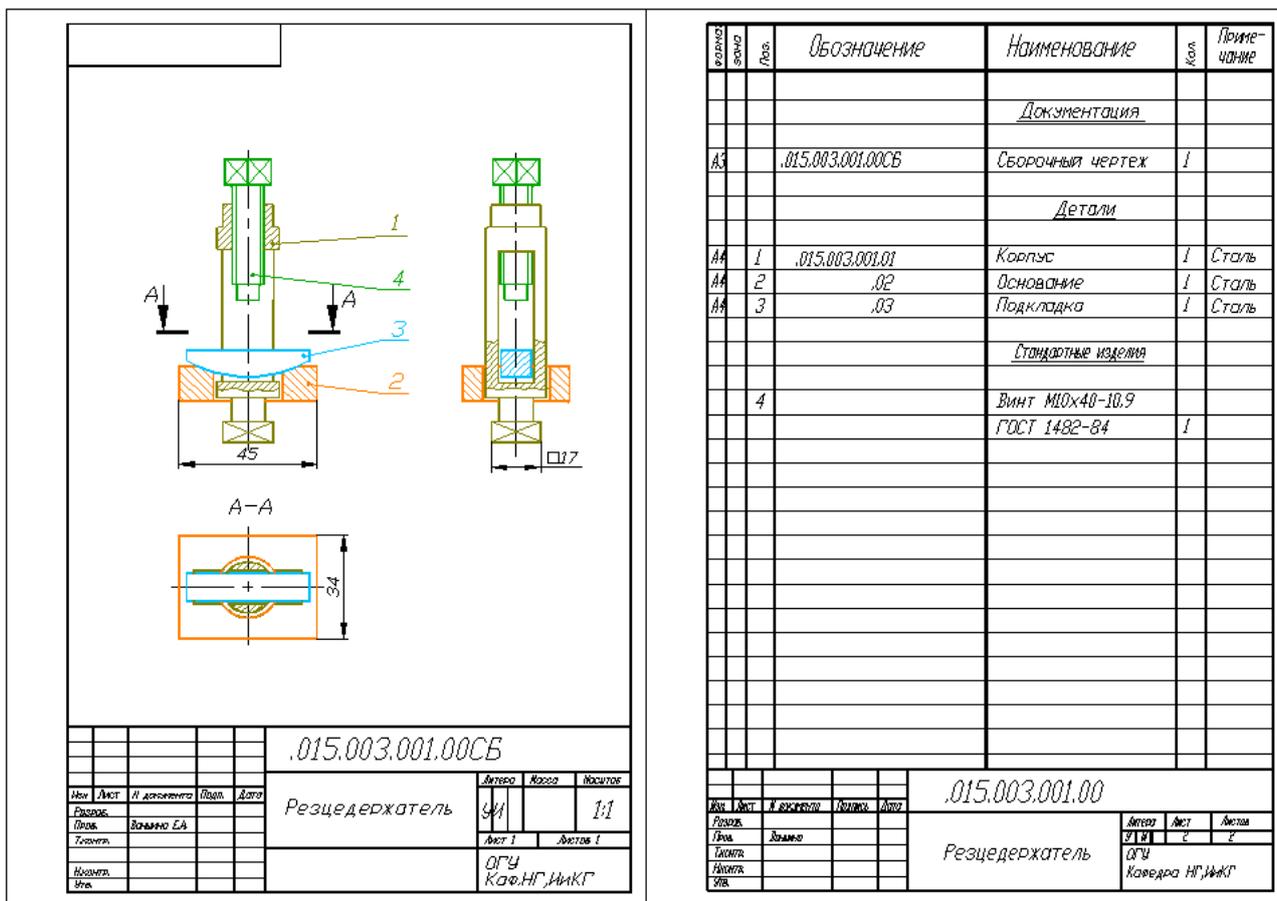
Сборочный чертеж «Резцедержатель».
